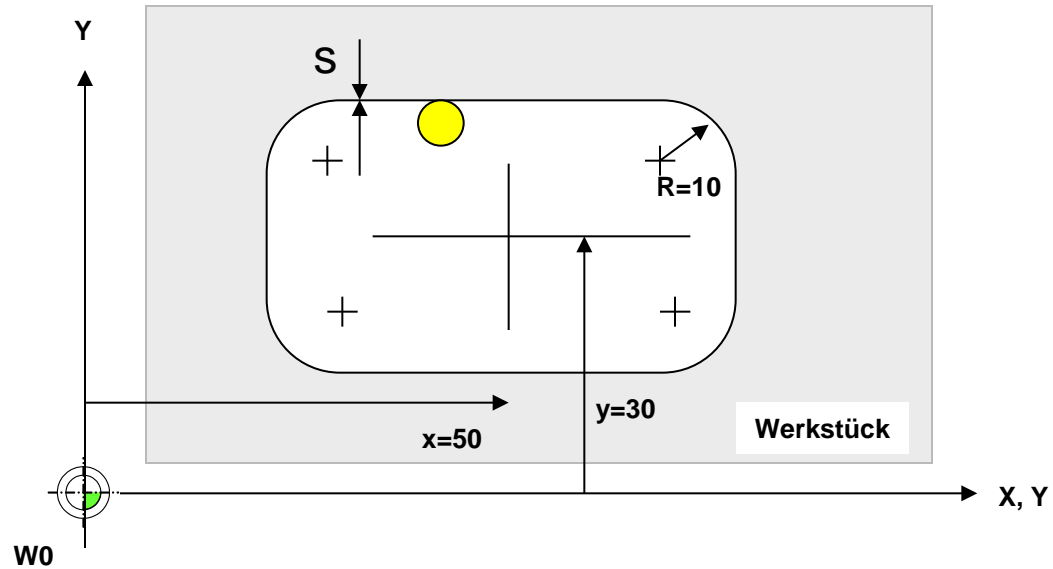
Parameter für die Definition einer rechteckigen Frästasche
